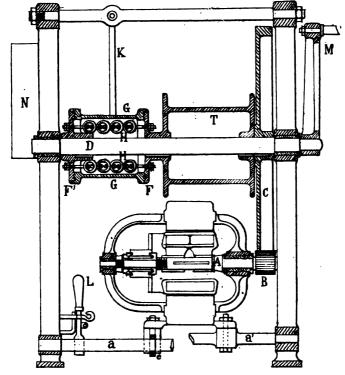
Treuil électrique escarbilleur à engrenages; disposition.
